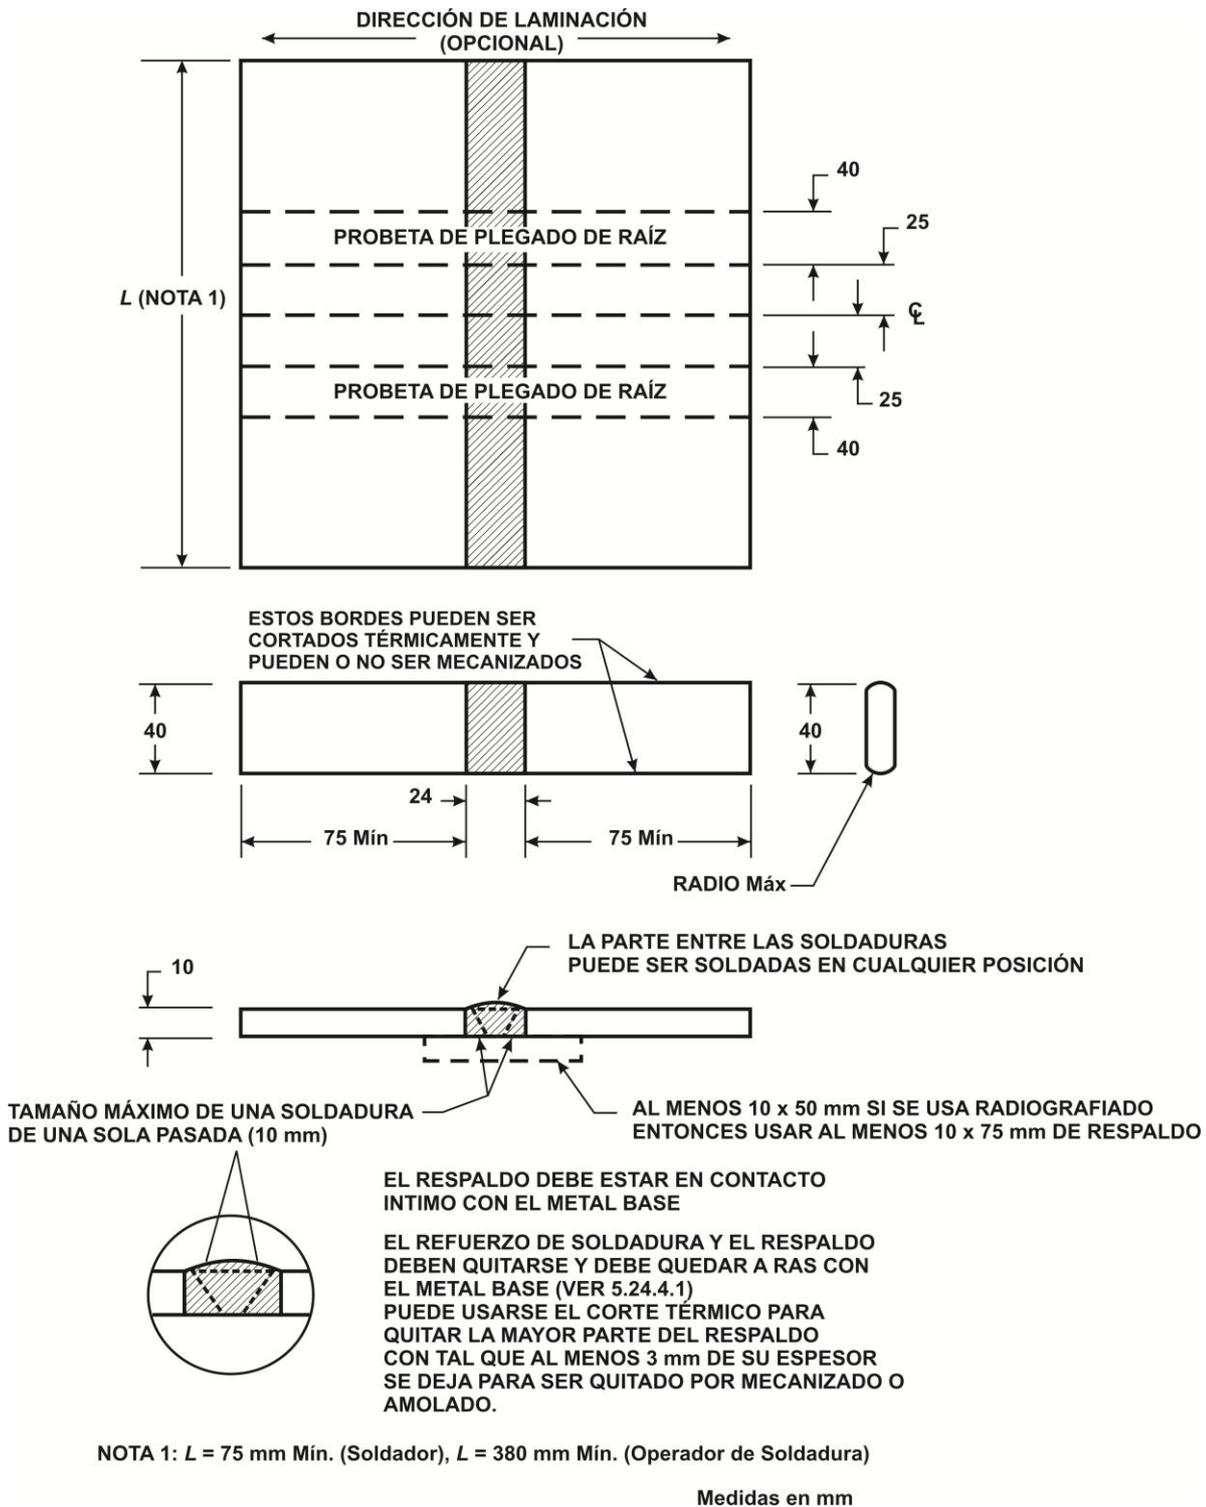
Chapa de Ensayo de plegado lateral para soldadura de filete – Calificación de soldador u operador – Opción 2.
